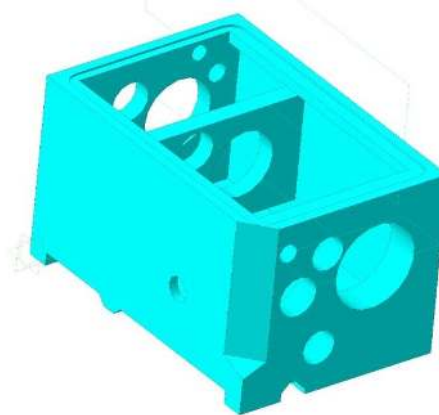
Корпус шпиндельной бабки станка с ЧПУ 16Б16Т1 (Россия)
